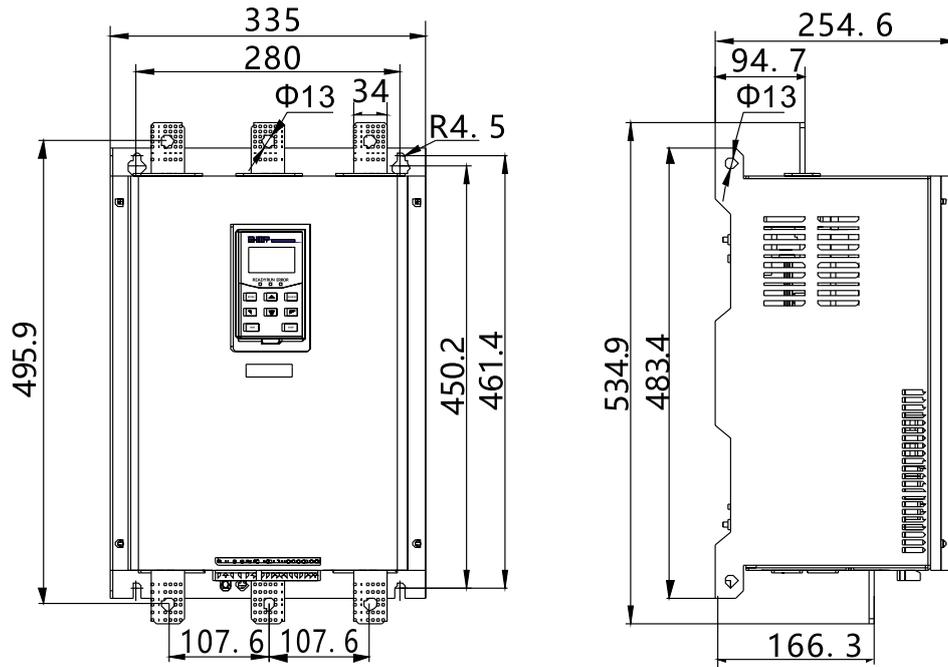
Общий компоновочный и установочный габаритный чертеж для устройств моделей NJR5-180/ZX3–NJR5-370/ZX3 и NJR5-180/ZX6–NJR5-370/ZX6
